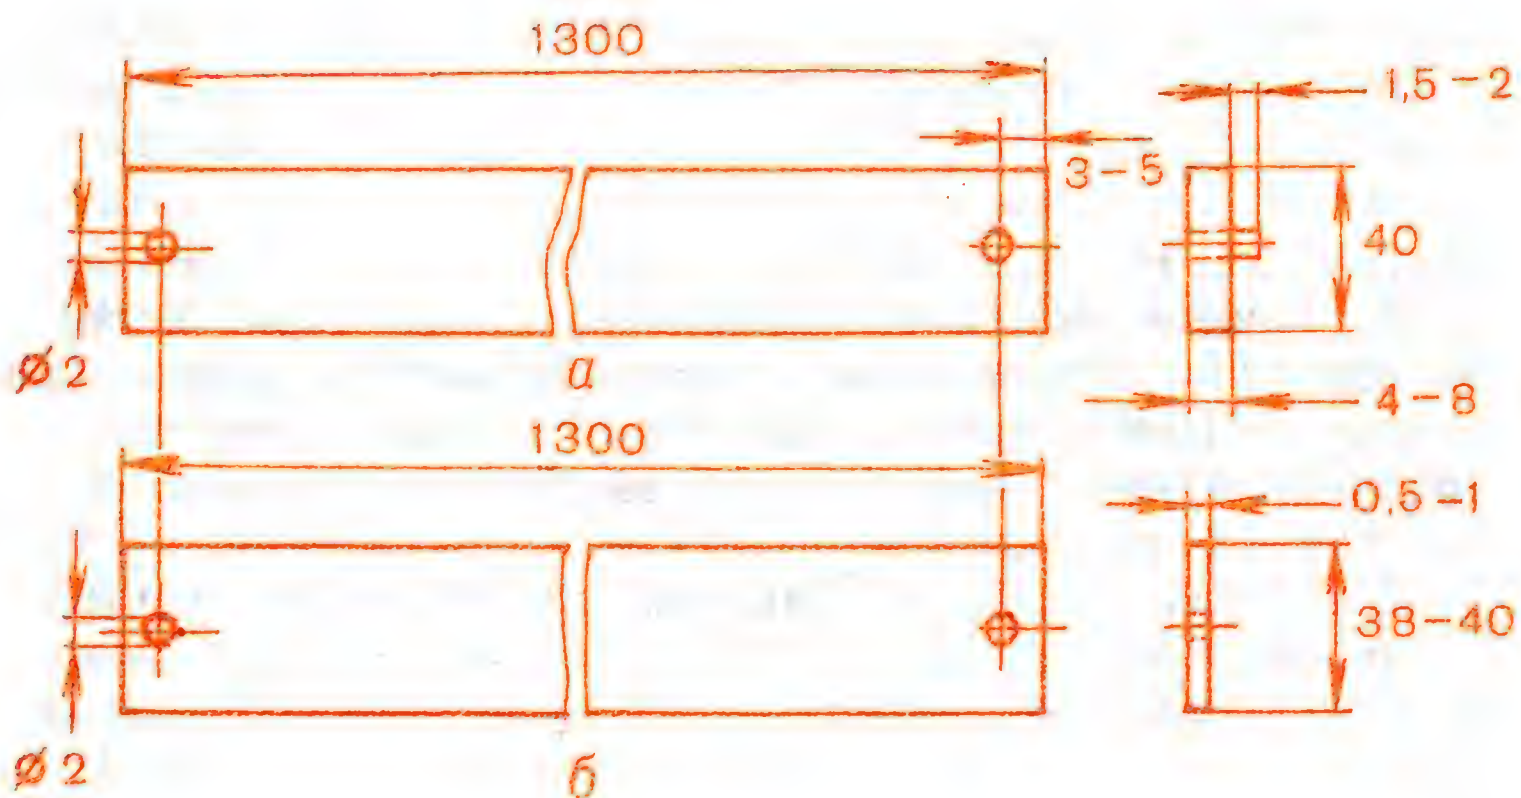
Детали фоторезака: а — режущая планка, б — прижимная линейка
